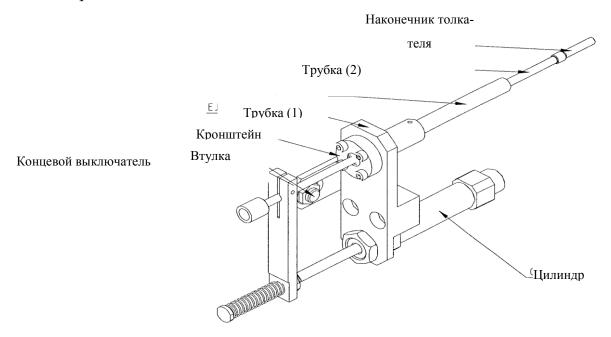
Приспособление для выталкивания деталей вперед/ обнаружения
